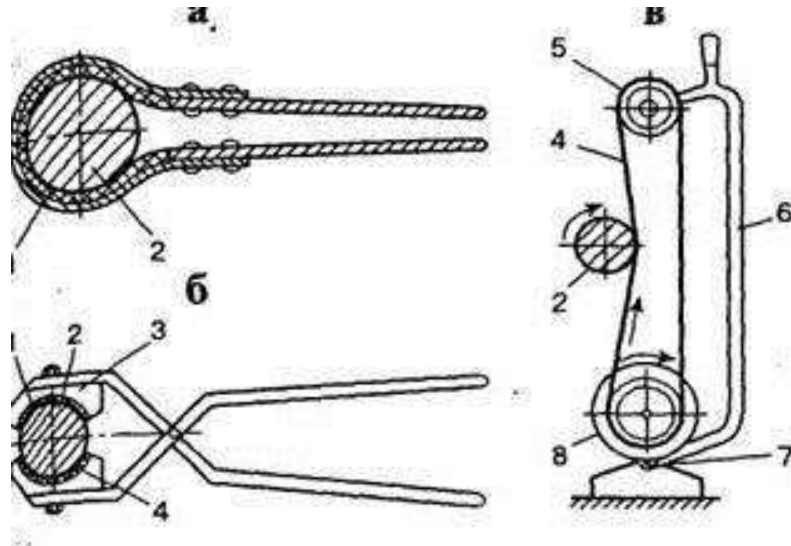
Пристосування для полірування шийок валів:
